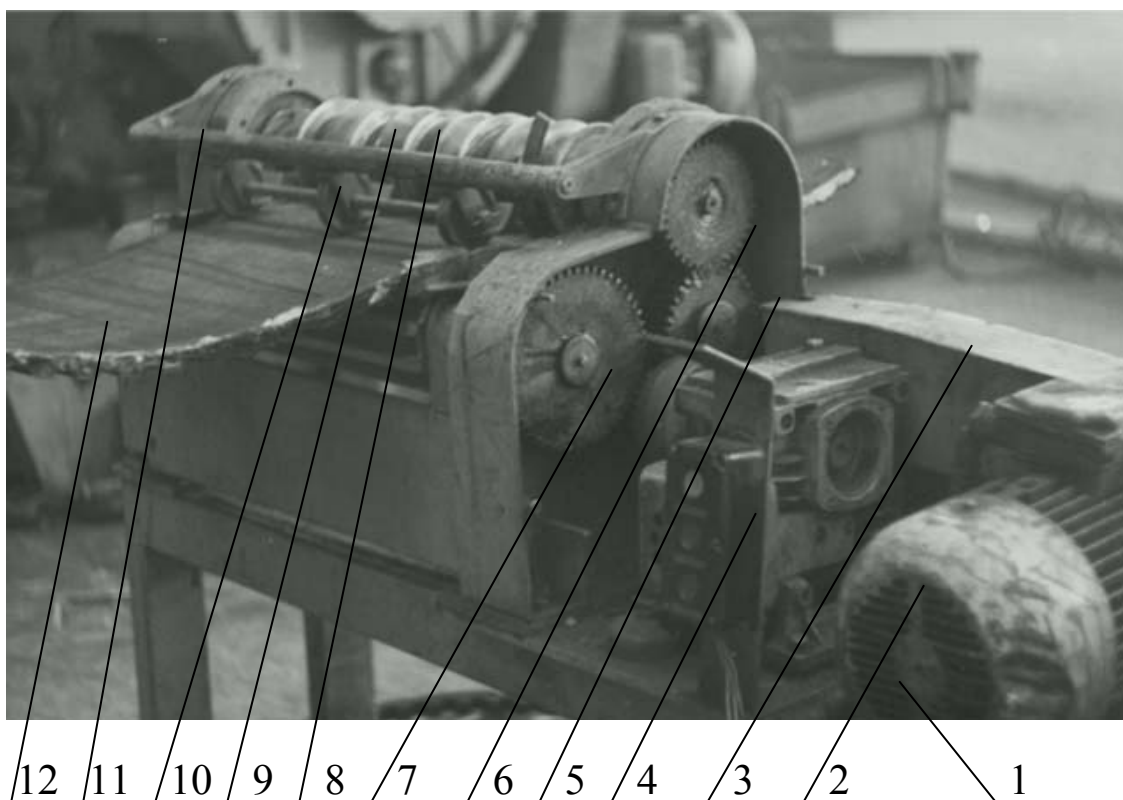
Загальний вигляд верстату для порізки конвеєрної стрічки з 5 ножовими блоками
